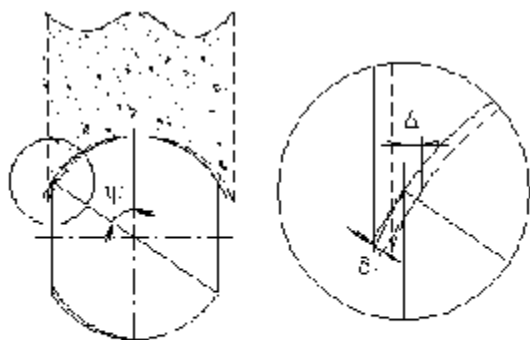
Схема обработки сферической поверхности методом профильного шлифования.
